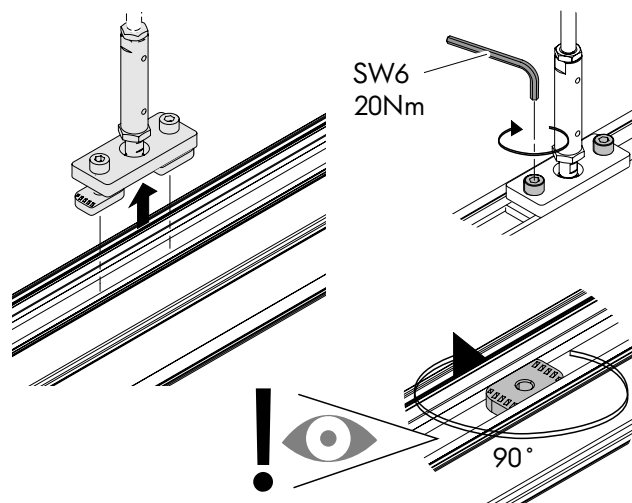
Montage du profilé à la suspension pendulaire de plafond
